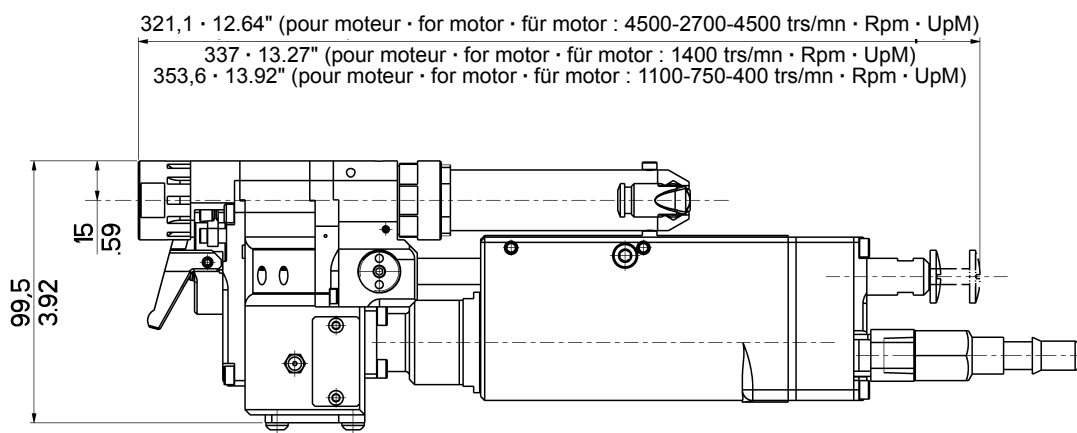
Machine 20942/20962 (côtes en mm) · Machine 20942/20962 (dimensions in mm) ·
